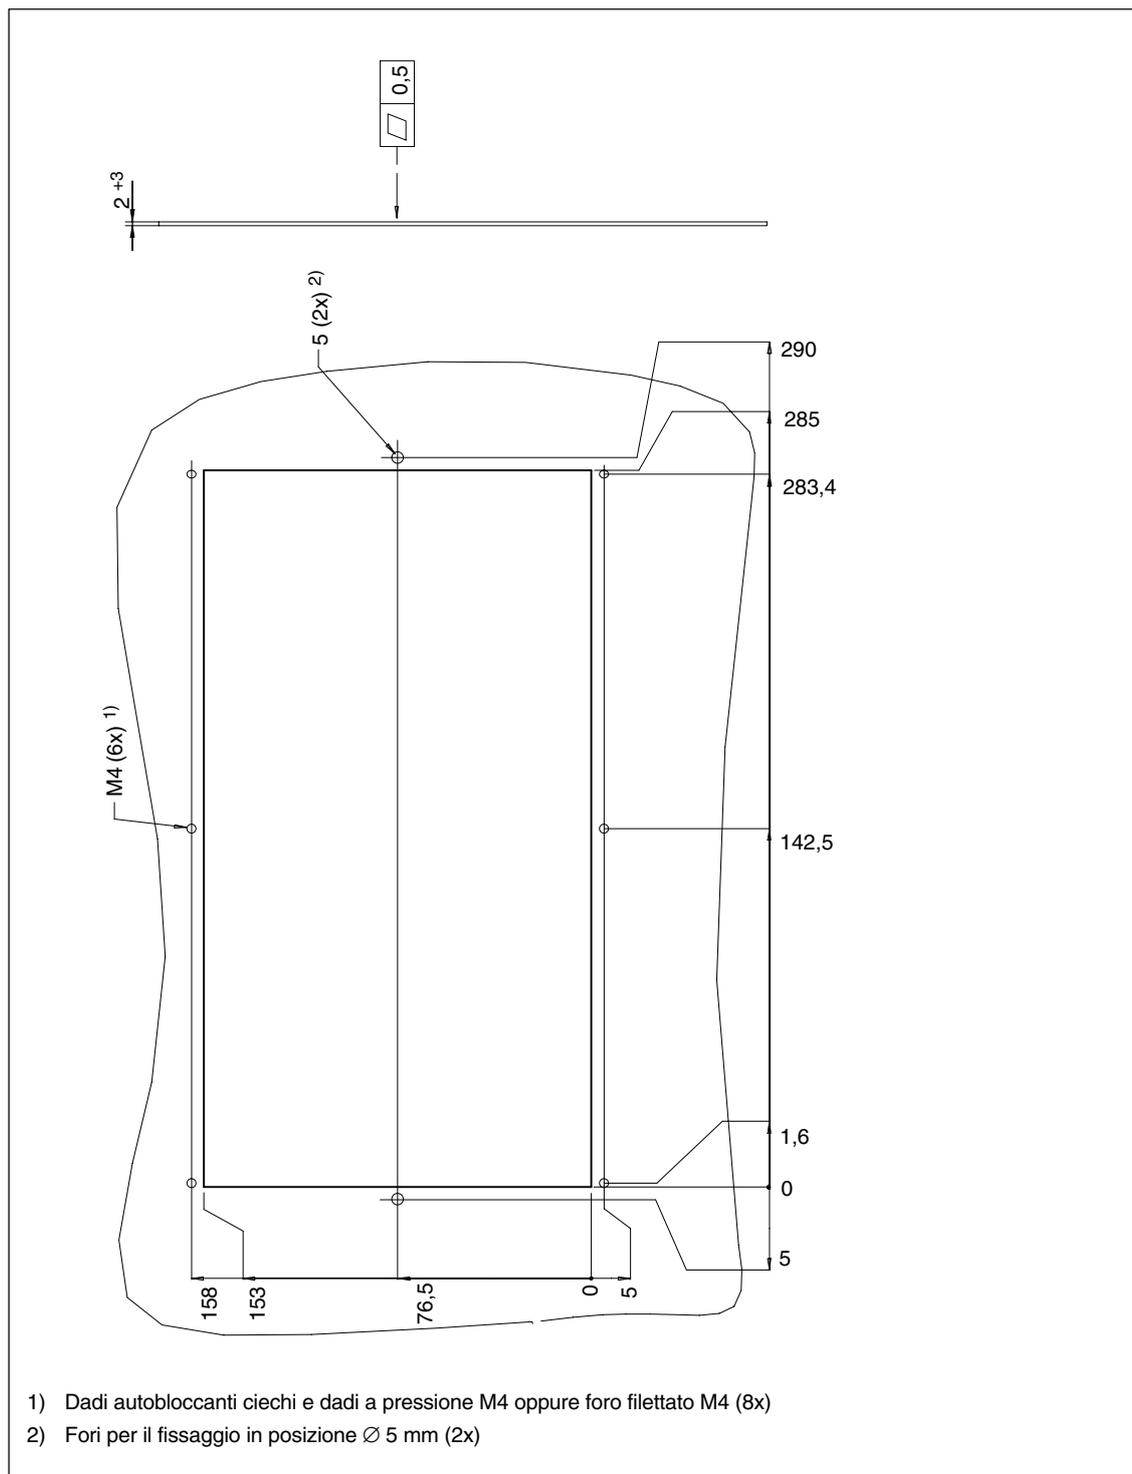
Schema di foratura della tastiera CN (montaggio sotto la PCU)
